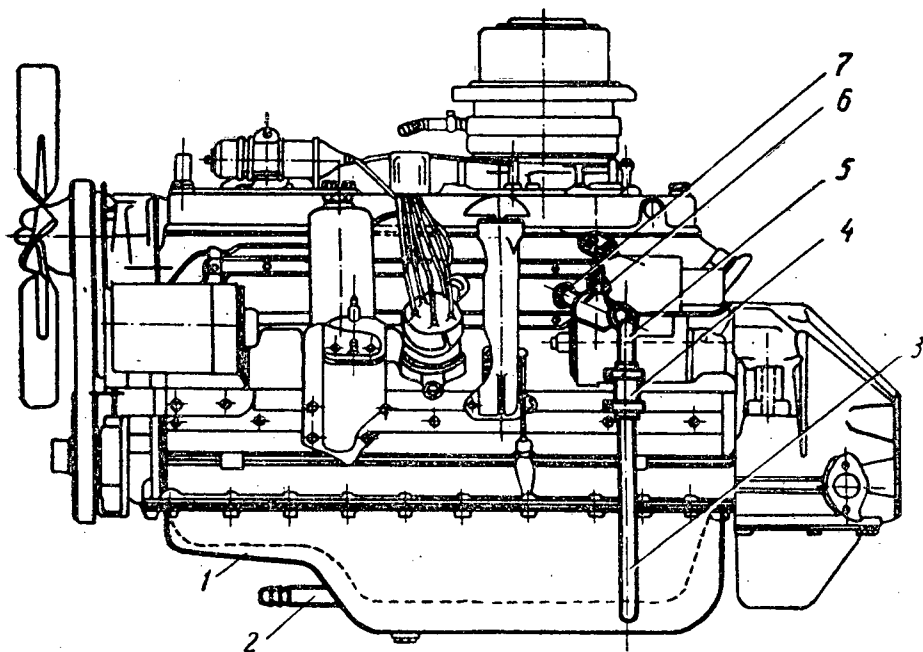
Общий вид двигателя ЗИЛ-120 с оборудованием для предпускового пароразогрева.
